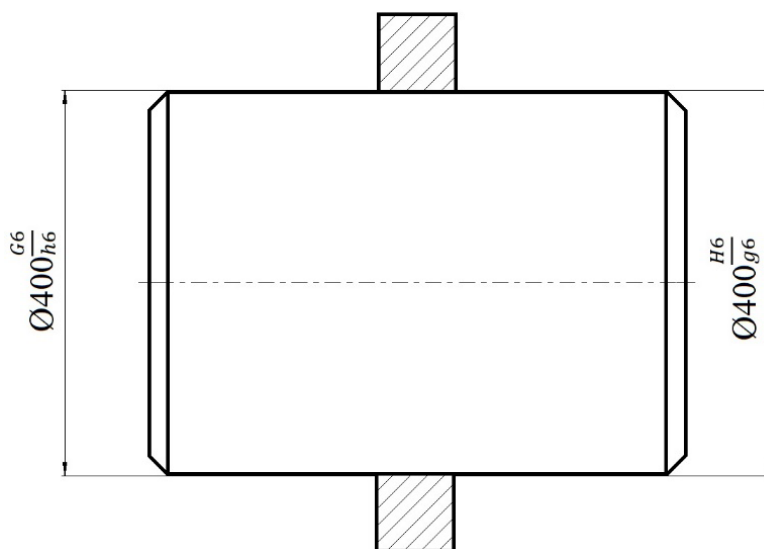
Сборочный чертеж гладкого цилиндрического соединения в системе отверстия и в системе вала
